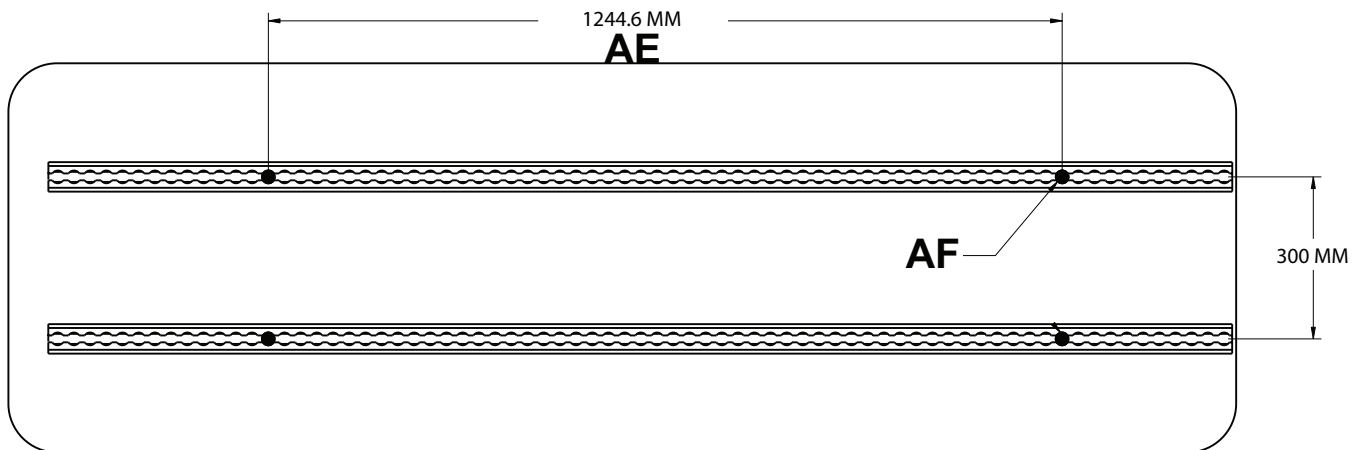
Posizioni per l'installazione delle piste a pavimento
